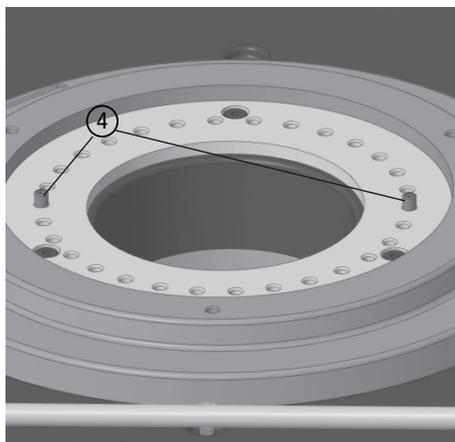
Goupilles de butée, réglage de la butée de fin de course gauche et droite
